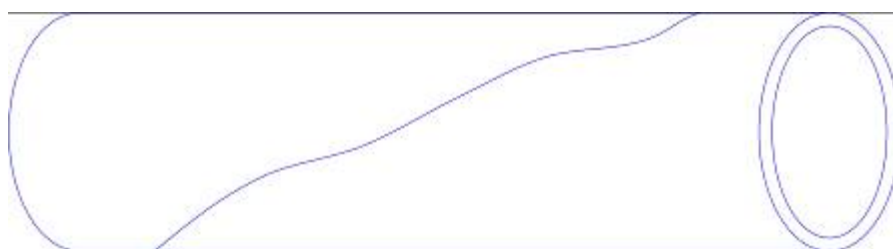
Сталеплавильная единичная плена на наружной поверхности, образующаяся при раскатывании продольной трещины слитка и заготовки (см. рисунок А.2, приложение А)
